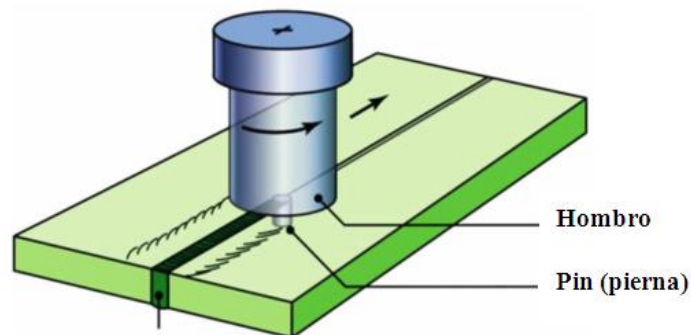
Esquema de la herramienta de soldadura
